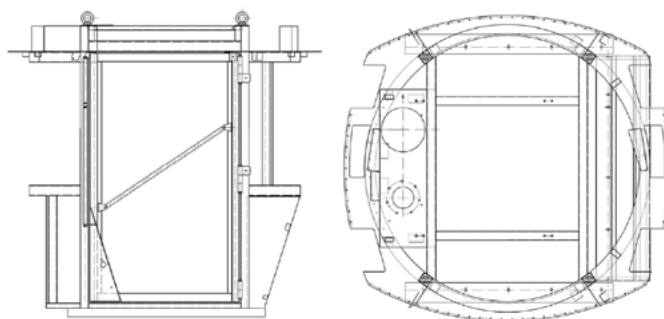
Несущий каркас кабины трактора ВТ-200: а — вид сбоку; б — вид сверху
